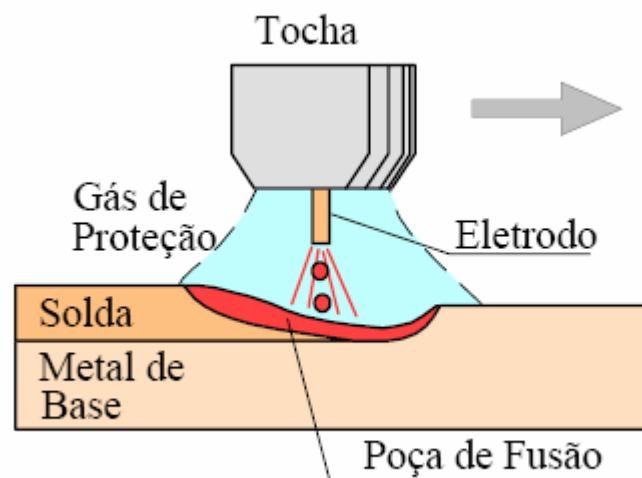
Esquema da tocha e a poça de fusão da soldagem MIG / MAG
